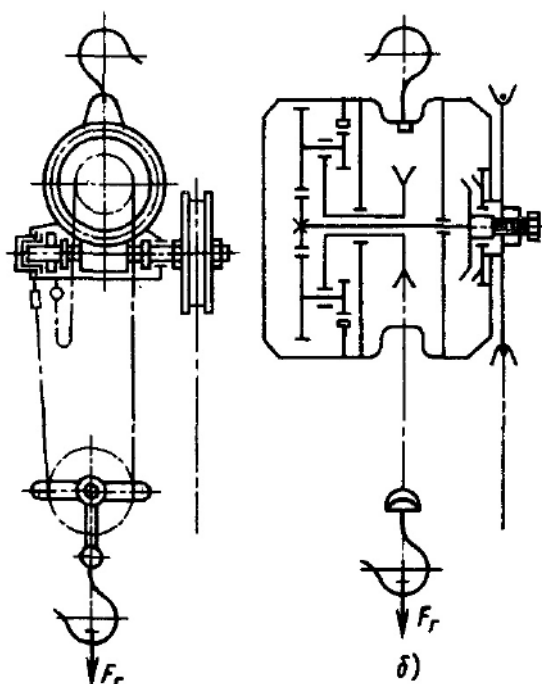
Схемы талей с ручным приводом: а - червячная; б - шестеренчатая
